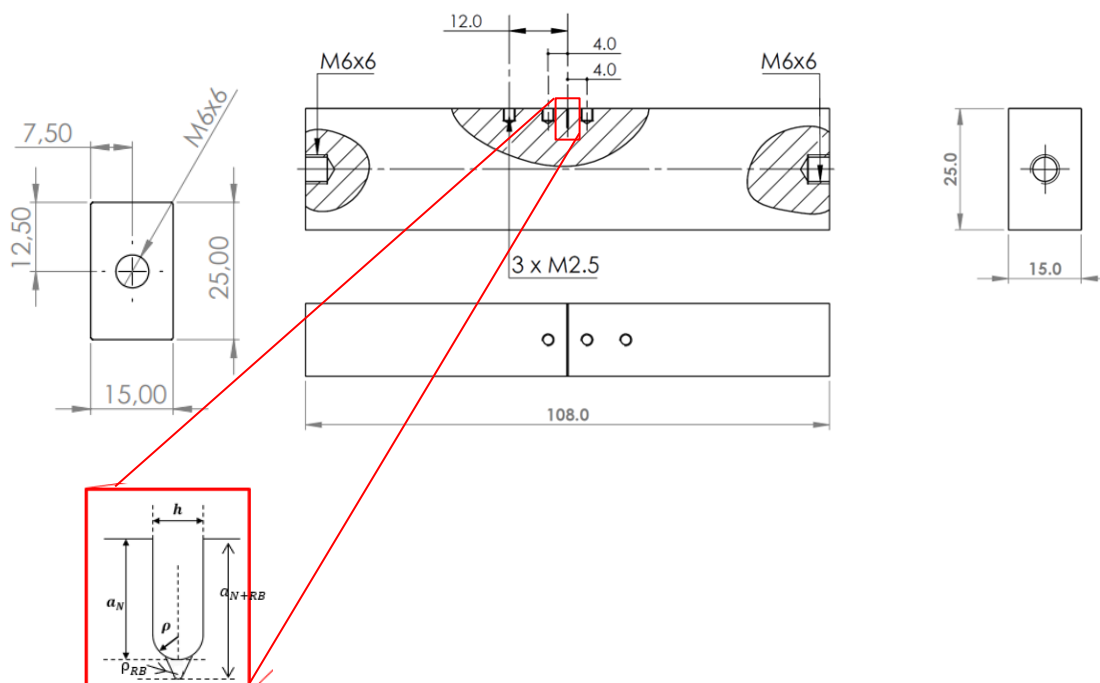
2: Disposizione dei collegamenti DCPD e geometria dell'intaglio post RB
